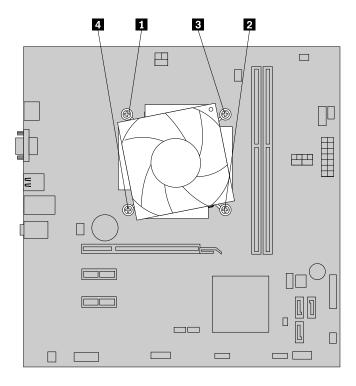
Removendo o Conjunto do Dissipador de Calor e do Ventilador
